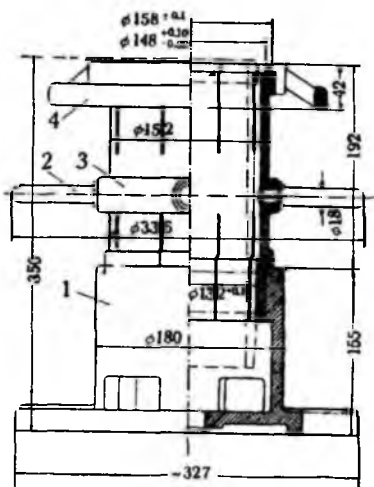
Приспособление для крепления гильз трактора СХТЗ на расточном и шлифовальном станках:
